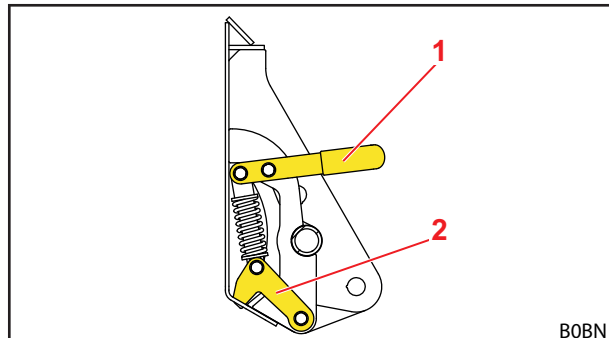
Mechanische Werkzeug-Verriegelung Skid-Steer (geöffneter Zustand)
